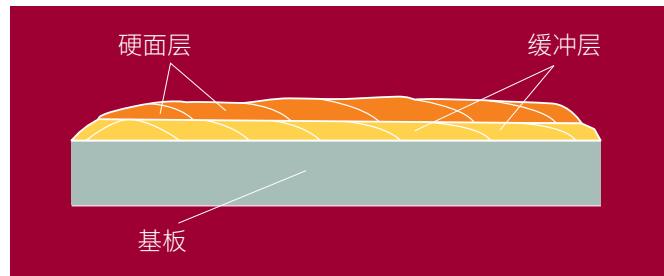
过渡层和表面耐磨堆焊的耗材的焊接顺序示例
